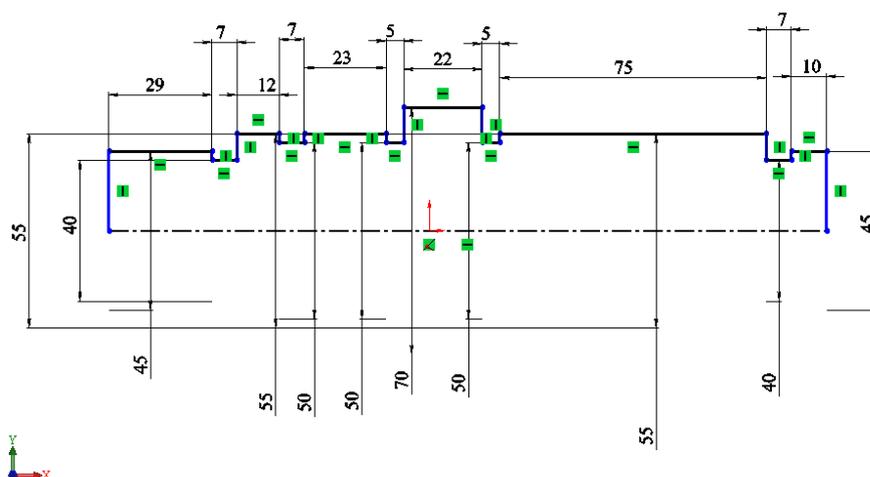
Ескіз для створення деталі обертання типу «Вал»
